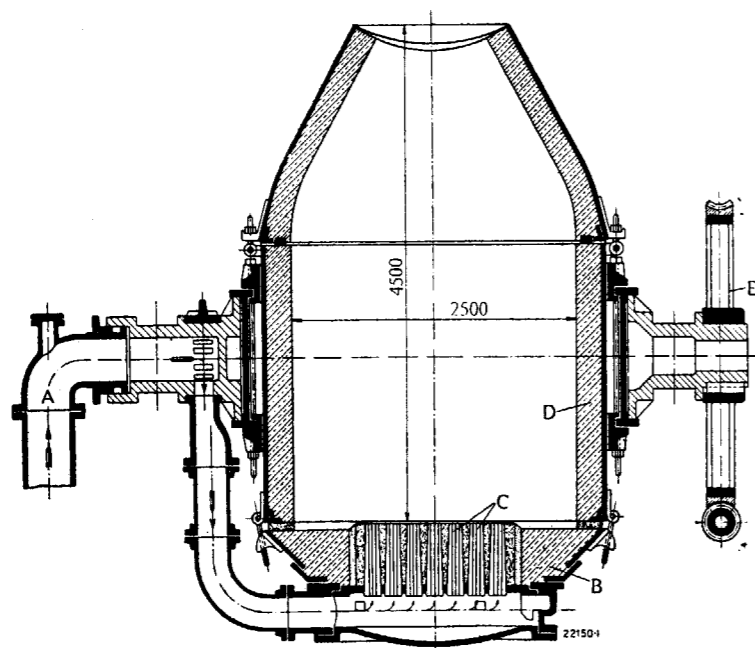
ª — Corte del convertidor Bessemer de una capacidad de 25 toneladas de la fábrica de Ebbw Vale (Inglaterra).
